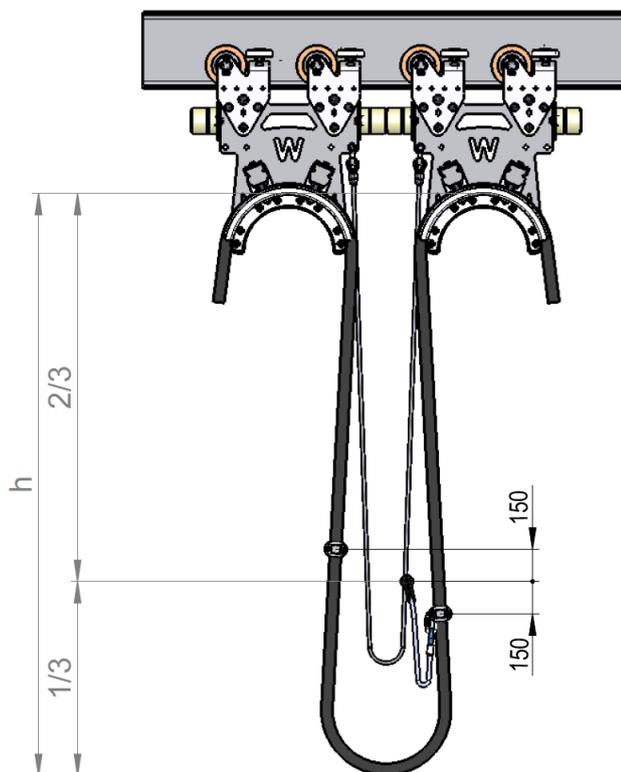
Posizione di montaggio dell'ammortizzatore a paravento
